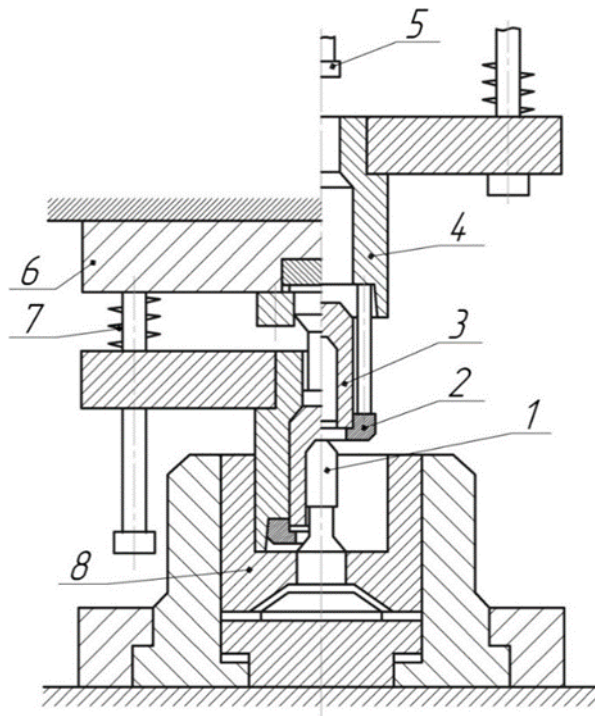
Промышленный штамп для прямого выдавливания деталей типа «стакан»: 1 - Пуансон; 2 - съемник; 3 - изделие; 4 - матрица; 5 - пуансон; 6 - верхняя плита; 7 - пружина
